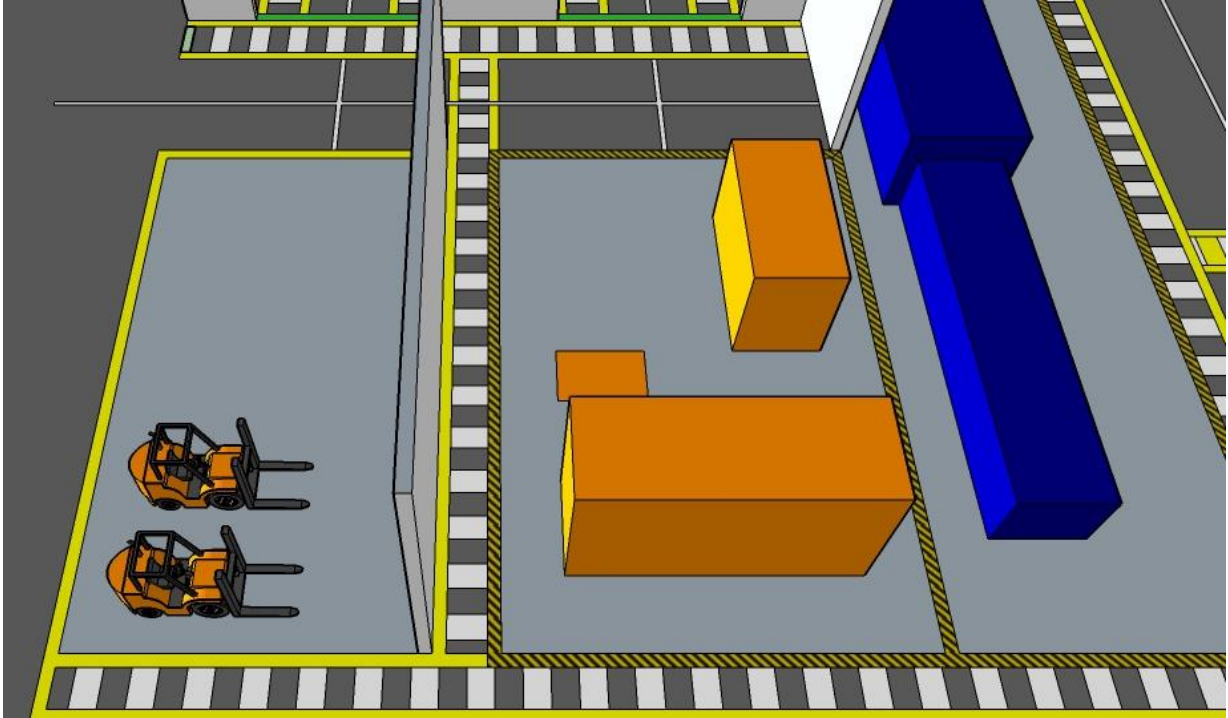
Zona de estacionamiento de autoelevadores y zona de corte, embalaje y paletizado
